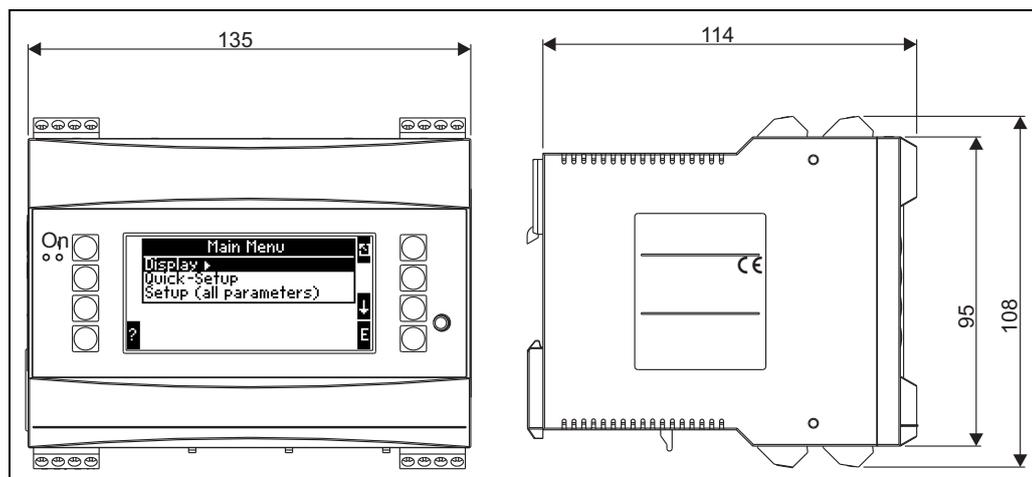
Корпус для монтажа на шину по IEC 60715; размеры даны в мм
